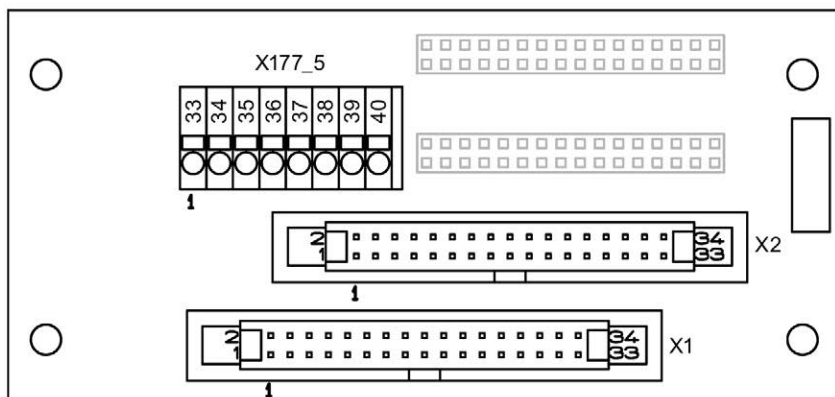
Disposición de bornes/conectores en la "Cabinet Board"
